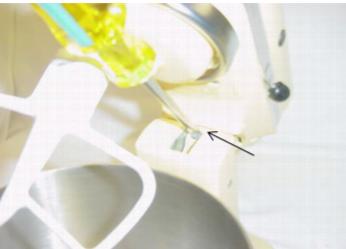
Le couvercle d'extrémité est fixé au mélangeur avec une vis à tête conique.
